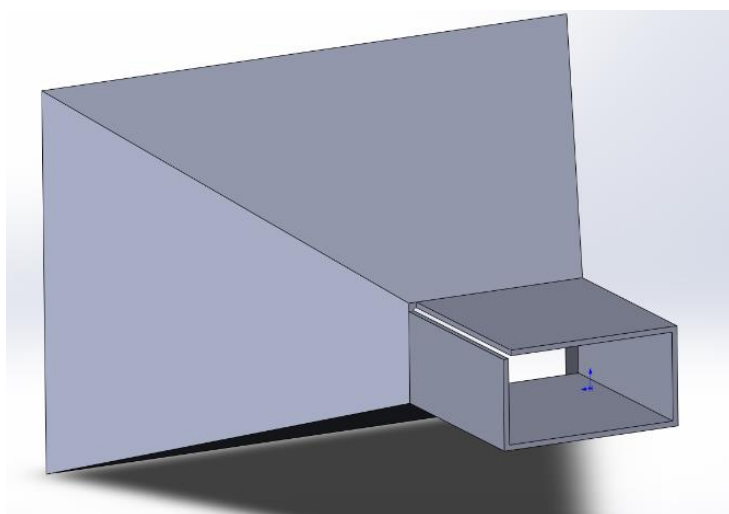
Рупор с дефектом сварного шва волновода.
